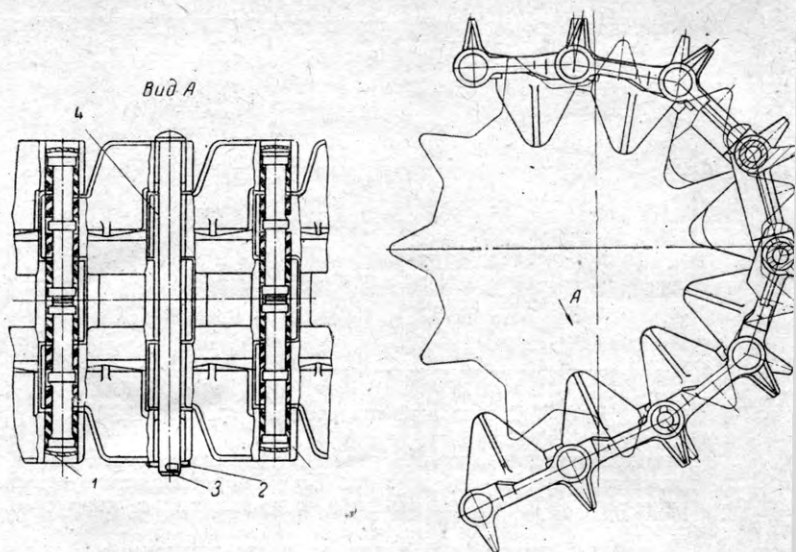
Схема гусеницы с резино-металлическими шарнирами: 1 — заглушка сферическая; 2 — шайба; 3 — шплинт; 4 — втулка замыкающего звена
